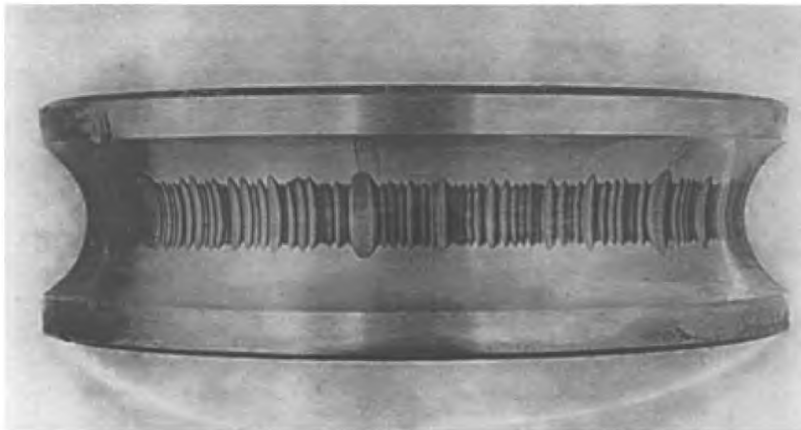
Появление бороздок из-за чрезмерного тока в подшипниках
